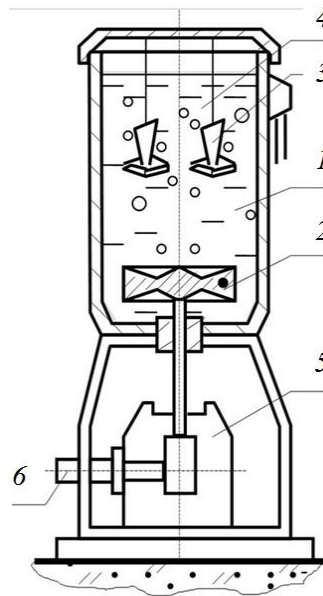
Установка для мийки: 1 – циліндрична ванна; 2 – диск-активатор; 3 – деталі, що промиваються; 4 – робоча зона ; 5 – вібраційний привод; 6 – двигун
